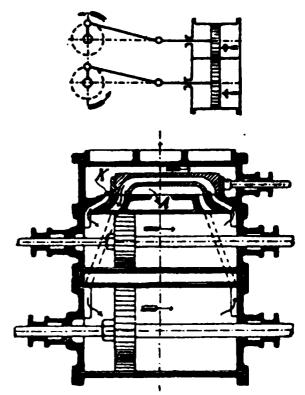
Gleichgerichtete Kolbenbewegung.
